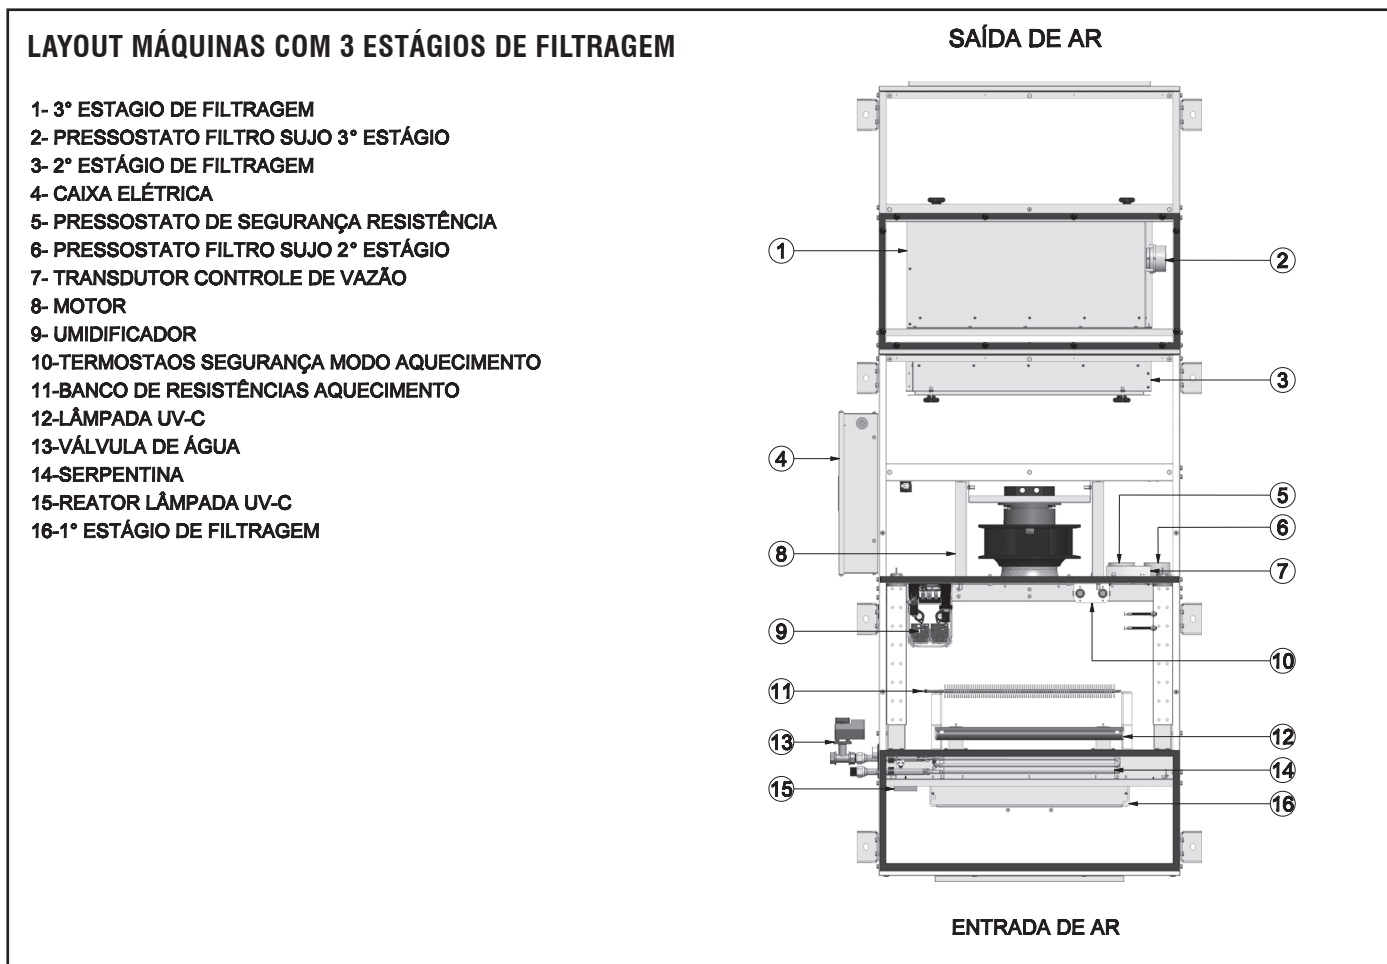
LAYOUT DOS COMPONENTES E OPCIONAIS: MÁQUINAS COM 3 ESTÁGIOS DE FILTRAGEM
